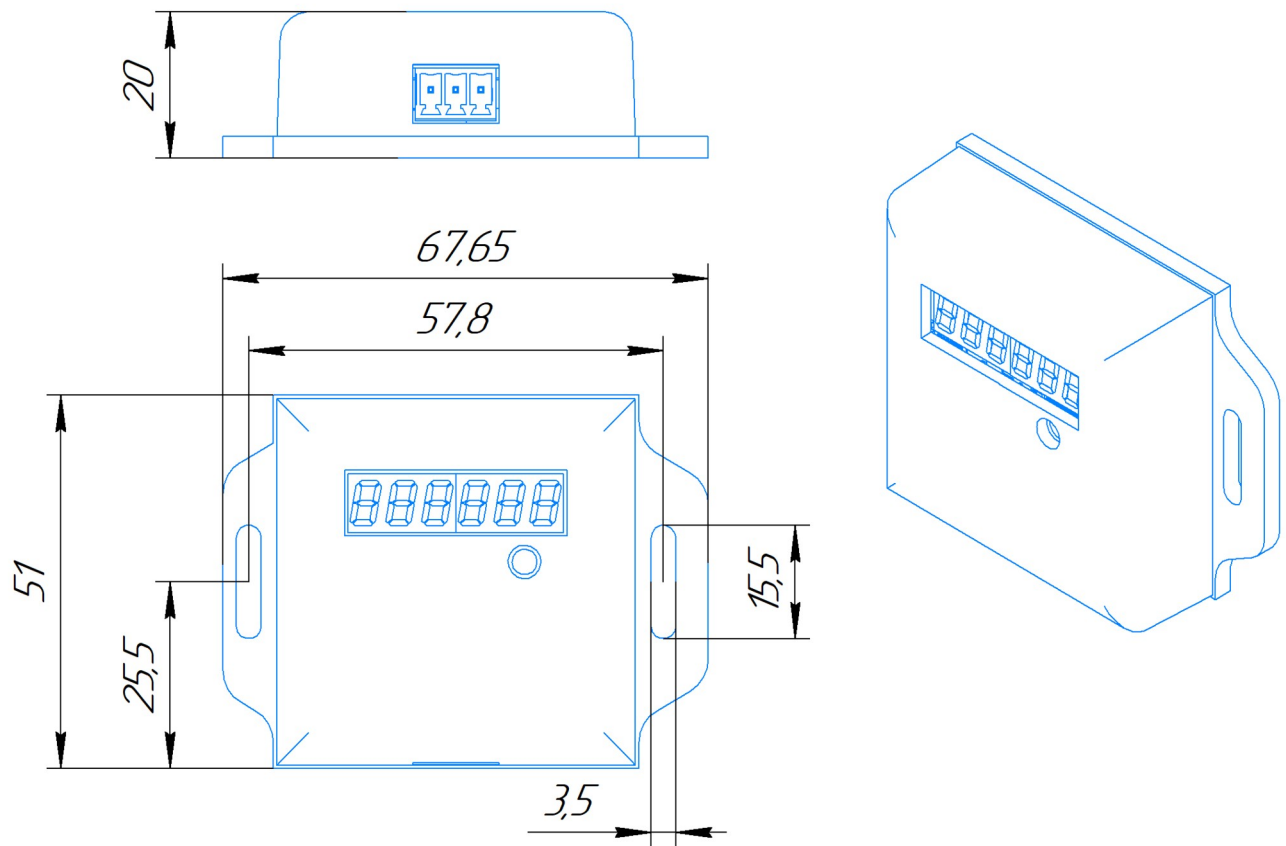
Габаритные размеры счётчика моточасов WTM-32
